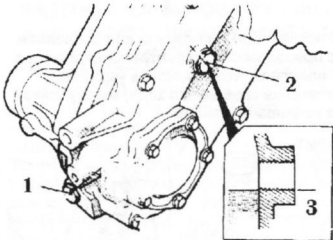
Местоположение заглушки передаточного кожуха
